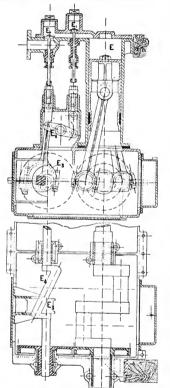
u. 5. Längsschnitt durch Cylinder und Steuerung, und Grundriss der Kurbelanordnung.
